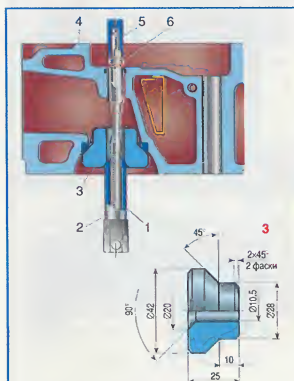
Запрессовка направляющей втулки клапана двигателя "Волги" ГАЗ-24: 1 – шпилька; 2 – гайка; 3 – опорная втулка; 4 – головка блока цилиндров; 5 – наконечник; 6 – втулка клапана.
